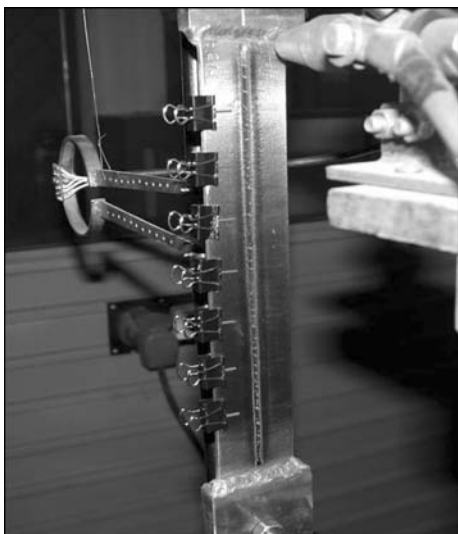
Общий вид образца после сварки на установке PVR-Test
